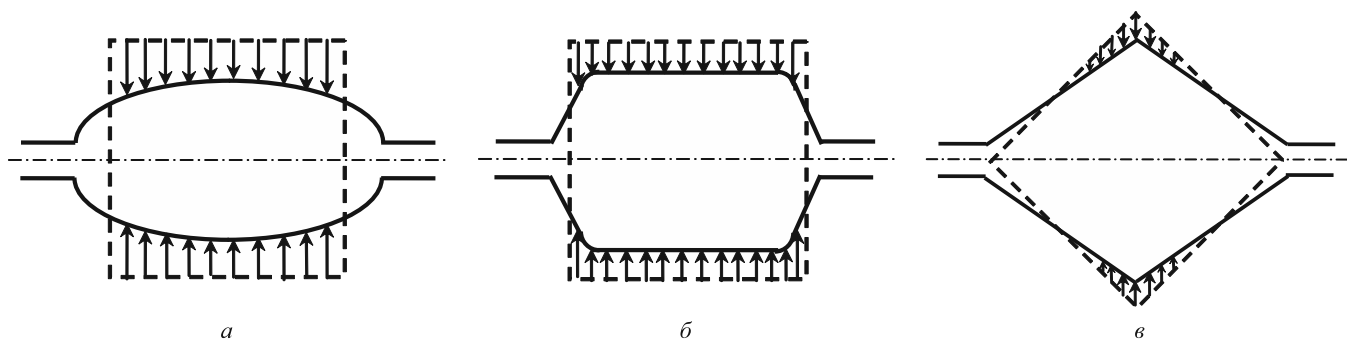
Схема распределения обжатий по ширине калибра при прокатке квадратной заготовки:
